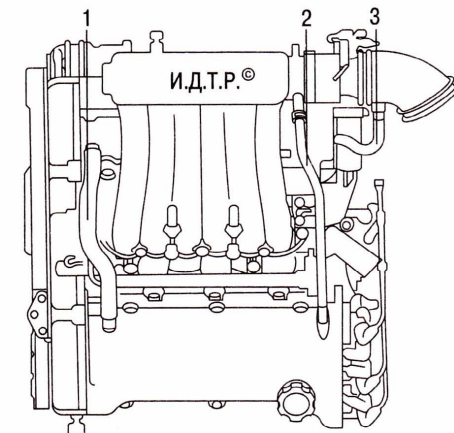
Трубопроводы системы вентиляции картера: 1 – соединительный трубопровод; 2 – трубопровод малой ветви системы вентиляции картера; 3 – трубопровод большой ветви системы вентиляции картера
